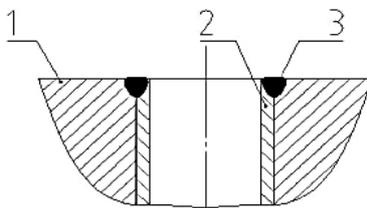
Расположение сварного шва (разрез): 1 – трубная решетка; 2 – труба; 3 – сварной шов
